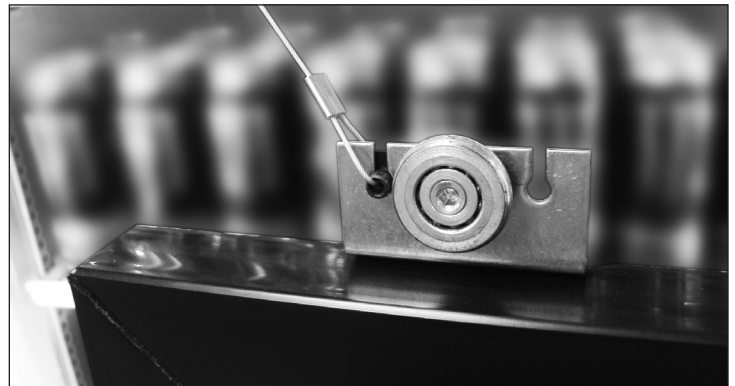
Die Türschnur muss in die Öse eingesetzt werden, die sich am dichtesten an der Laufrolle befindet
